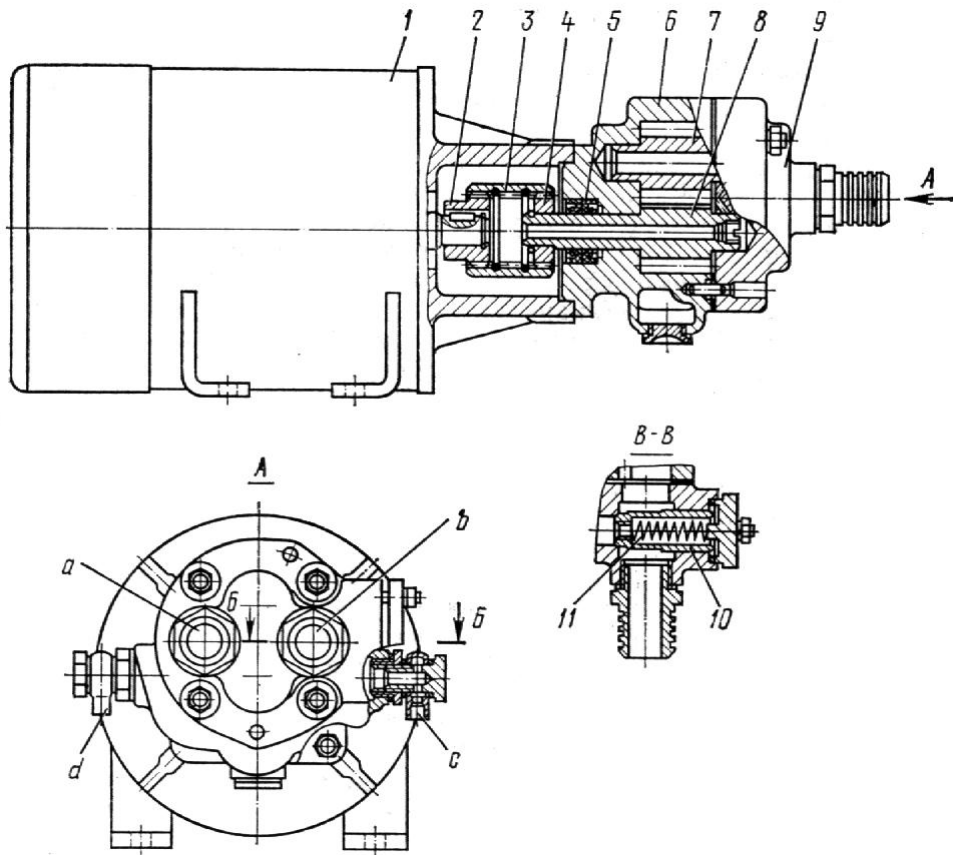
Агрегат маслозакачивающий: 1 – электродвигатель; 2 – втулка ведущая; 3 – муфта; 4 – втулка ведомая; 5 – манжета; 6 – корпус; 7 – шестерня ведомая; 8 – шестерня ведущая; 9 – крышка; 10 – клапан; 11 – пружина редукционного клапана; а – подвод масла; б – отвод масла; с – отвод воды; д – подвод воды
